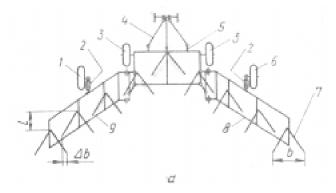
Схема культиватора-плоскореза: 1 и 6 — самоустанавливающиеся колеса; 2— гидроцилиндры; 3— неповоротные колеса; 4— навеска; 5, 8 и 9— средняя, правая и левая секции; 7— плоскорежущие лапы
